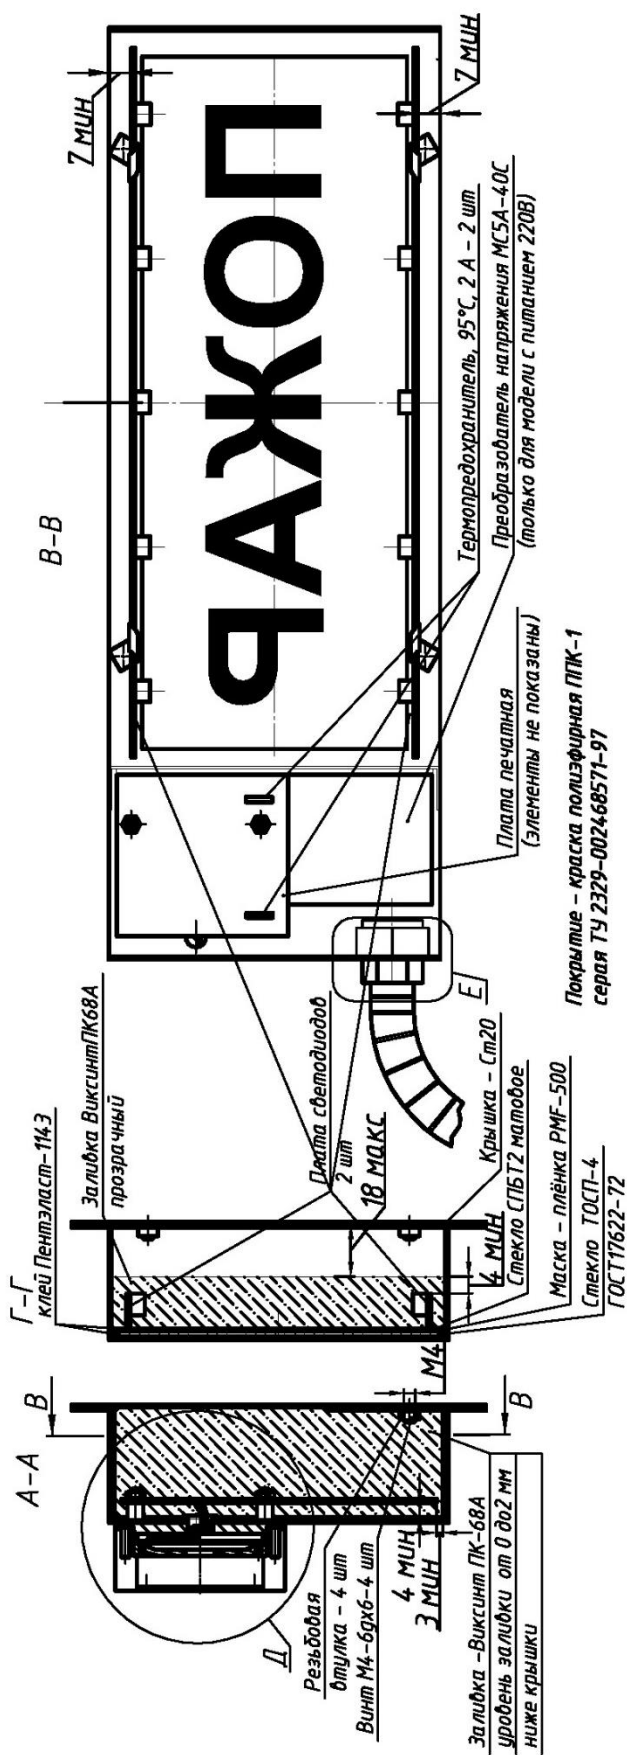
Габаритный чертёж световых табло Филлин-Г -М-12-БЗ, Филлин-Г-М-220-БЗ, Филлин-Г-Б-12-БЗ и Филлин-Г-Б-220-БЗ (без звука) с элементами взрывозащиты, кабель в металлокаве, остальное см. на рисунках А.1, А.3, А.4. Для моделей с питанием постоянным напряжением провод "+" кабеля питания отмечен красным цветом
